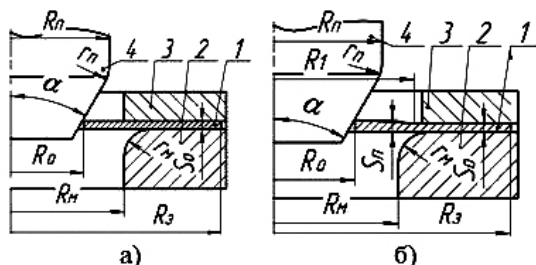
Схемы отбортовки: а - традиционной заготовки; б - спрофилированной заготовки
